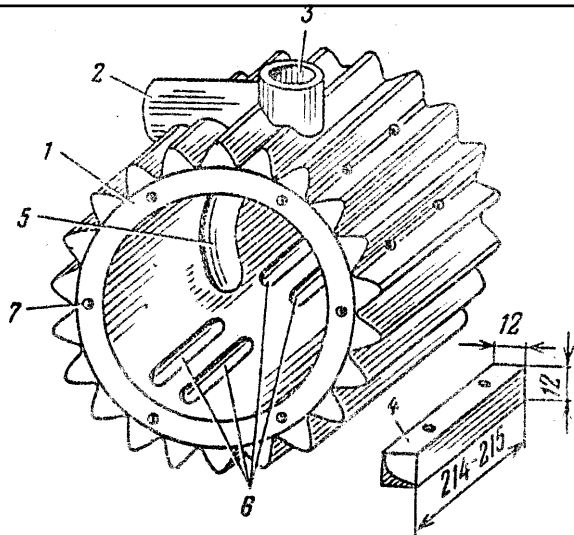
Внутренний вид статора крупорушки (без ротора): 1 - статор; 2 - патрубок (нерабочий); 3 - патрубок (рабочий); 4 - стальной вкладыш (2 шт.) затемненный угол стачивается при установке зазора между ротором и вкладышем; 5 - углубление во внутренней стенке статора (заводское); 6 - прорези (окна) сквозные для выхода размоленного зерна (4 шт.); 7 - отверстие для установочного (фиксирующего) штифта
